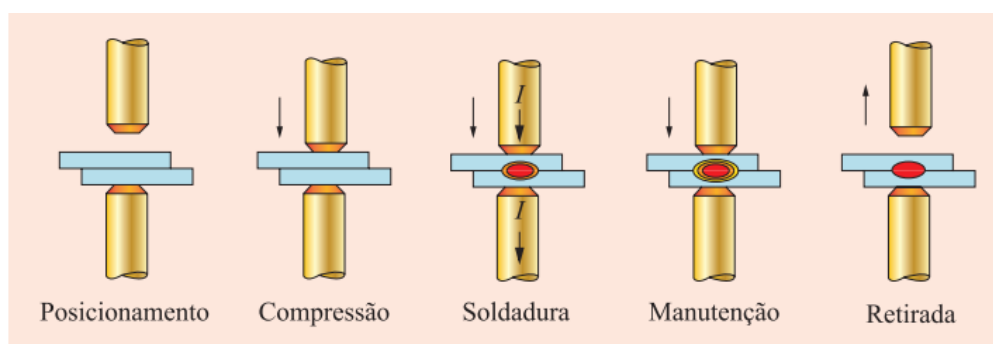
Diferentes etapas de realização de uma soldadura por pontos (Retirado de: Silva, 2016)
